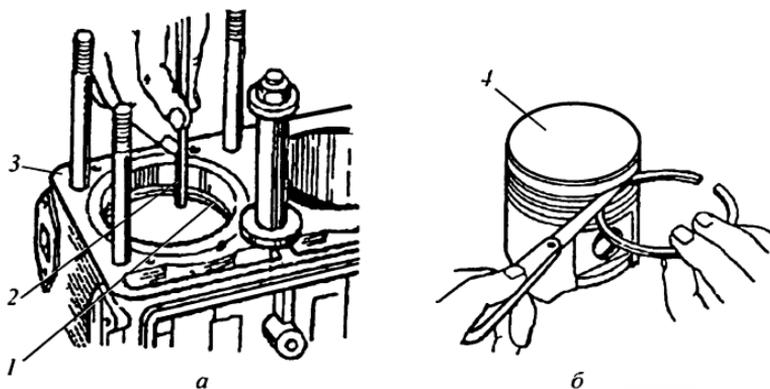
Проверка зазора в замке поршневого кольца (а) и бокового зазора между поршневым кольцом и канавкой в поршне (б): 1 — поршневое кольцо; 2 — щуп; 3 — блок цилиндров двигателя; 4 — поршень
